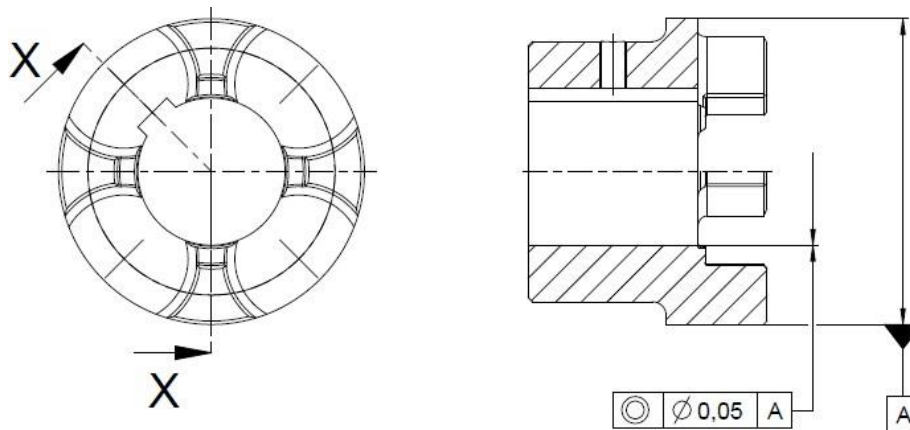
Допуск формы и положения отверстия и положения шпоночного паза.
